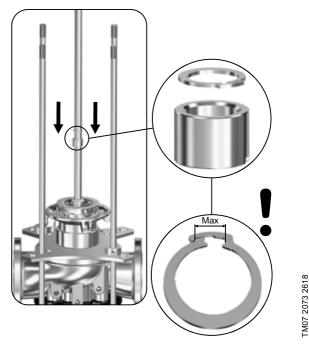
Установка рабочего колеса (49 или 49а) на валу насоса (51) при помощи приспособления С
